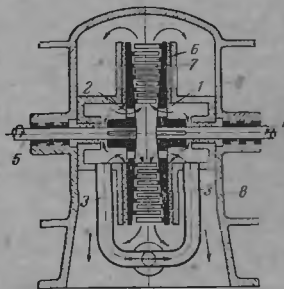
Принципиальная схема радиальной турбины. 1 и 2 — диски; 3 — подвод свежего пара; 4 и 5 — валы; 6 и 7 — рабочие лопатки; 8 — корпус.
